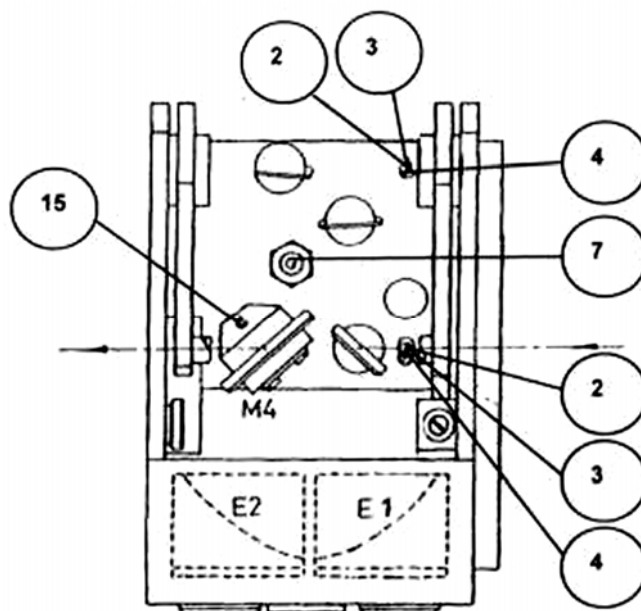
Вид сверху приставки для направления луча справа налево
